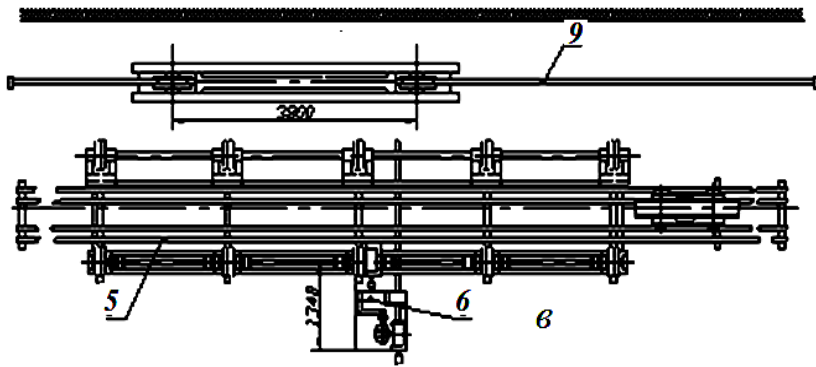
Установка для автоматичного зварювання поздовжніх і кільцевих швів котлів цистерн зварювальним трактором:
